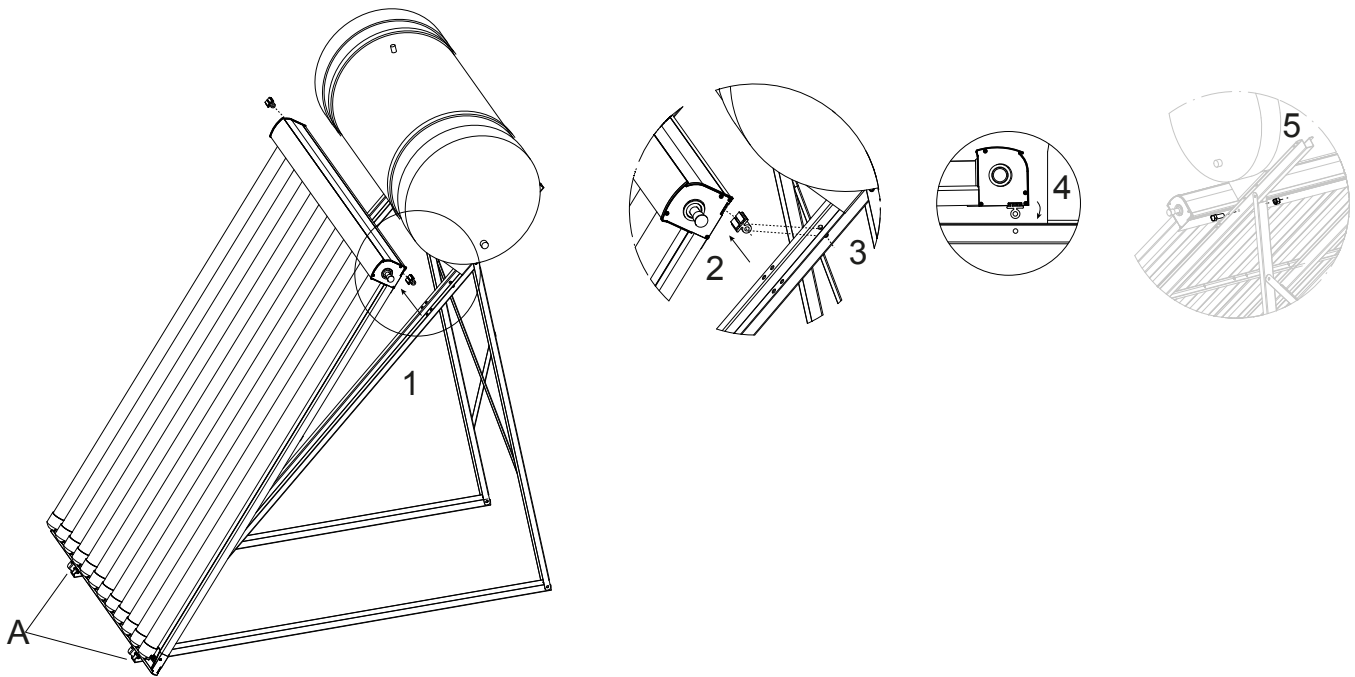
Montaggio staffe per fissaggio fasce
